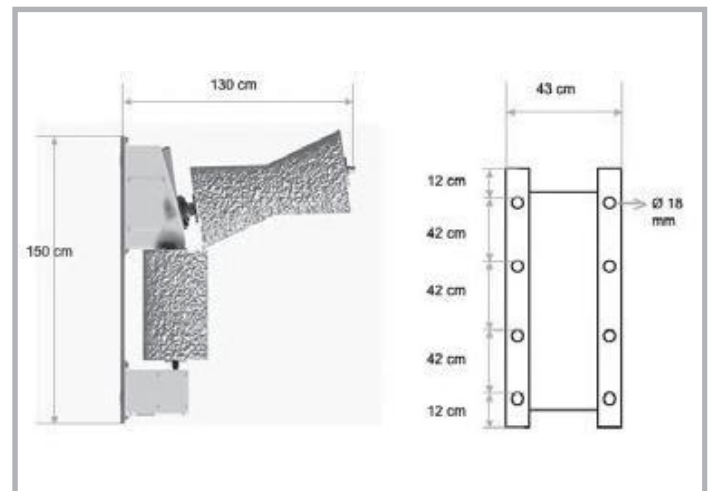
RotaBrush Twin: Montiert mit Installationsmaßen
